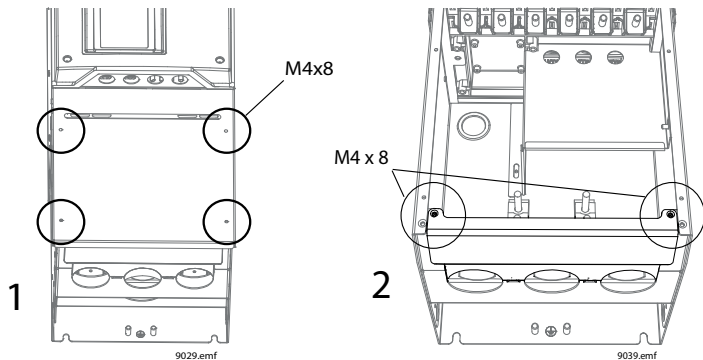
Retirar a tampa dos cabos e a placa de fixação dos cabos (MR8).
